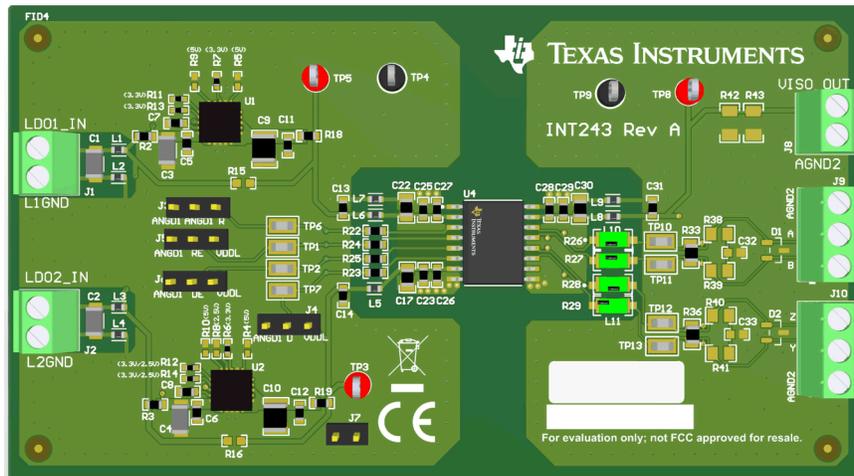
ISOW380DWEEVM PCB 3D 视图 - 顶层
